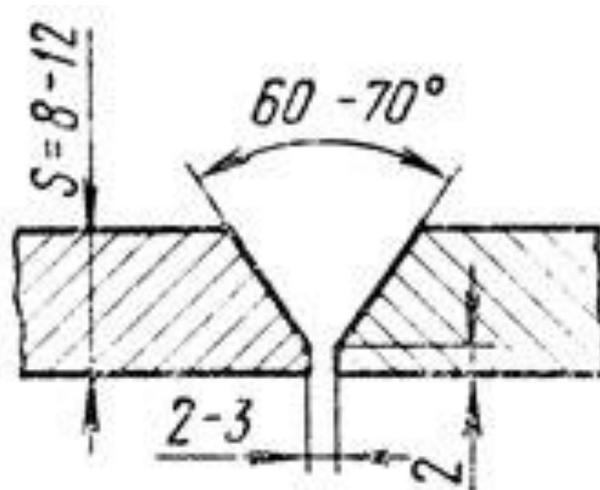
подготовка кромок труб под сварку при толщине стенок 8-12 мм
